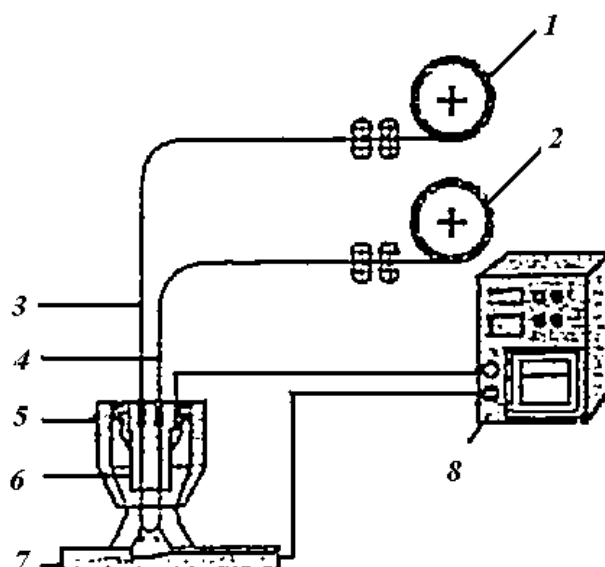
Схема тандемной МИГ-сварки:
